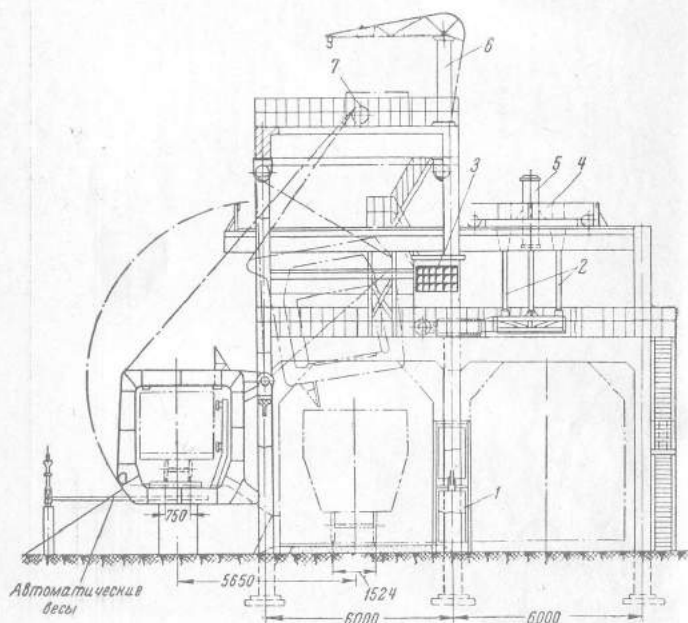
Башенный вагоноопрокидыватель для торфа.
